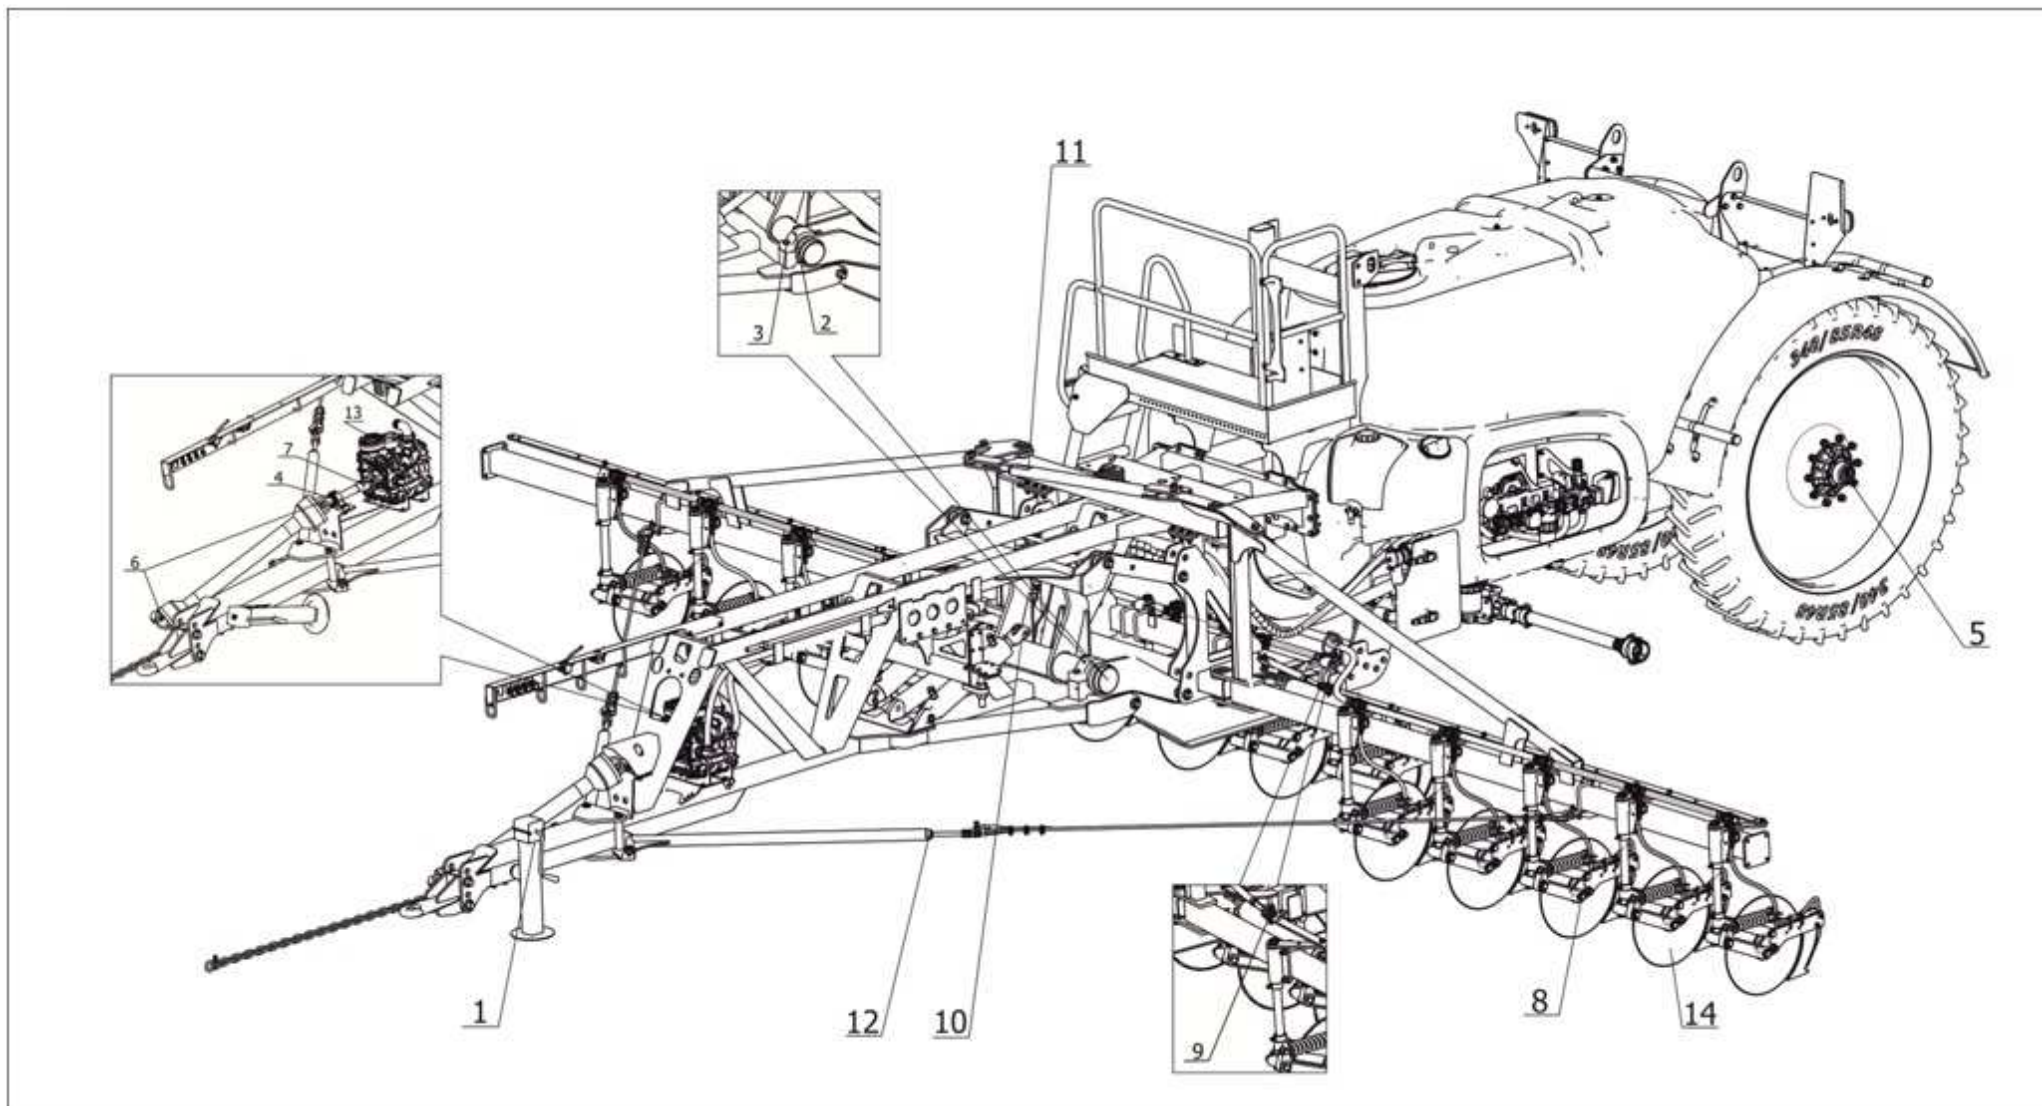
Смазка аппликатора AP-3000/13
